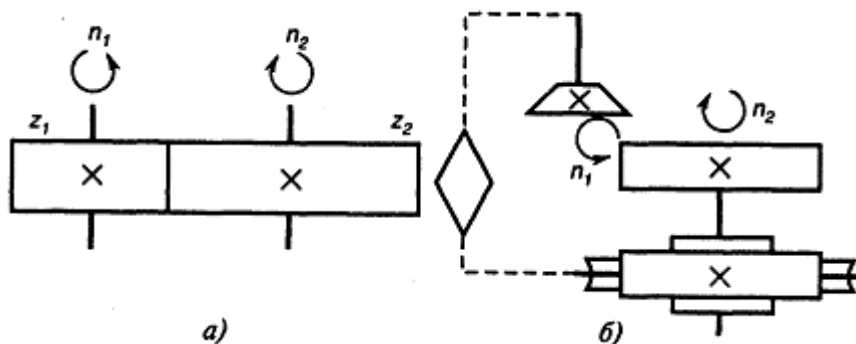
обкатки двох зубчастих коліс (а), інструменту та заготовки (б)
